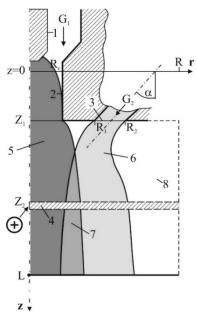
Схема процесса плазменно-дугового проволочного напыления: 1 — катод; 2 — сопло; 3 — канал подачи обдувающего газа; 4 — проволока-анод; 5 — дуговая плазма; 6 — обдувающий газ; 7 — область смешения; 8 — внешняя газовая среда
